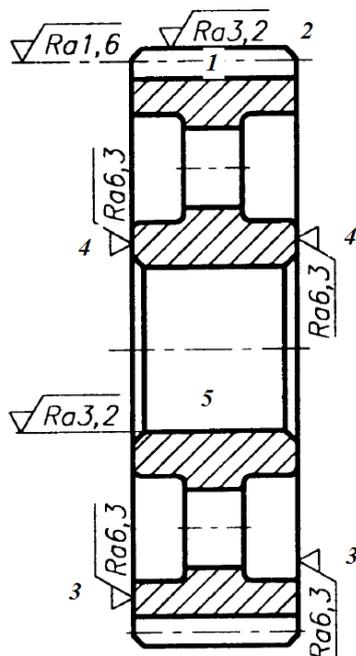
Обозначение шероховатости зубчатого колеса
